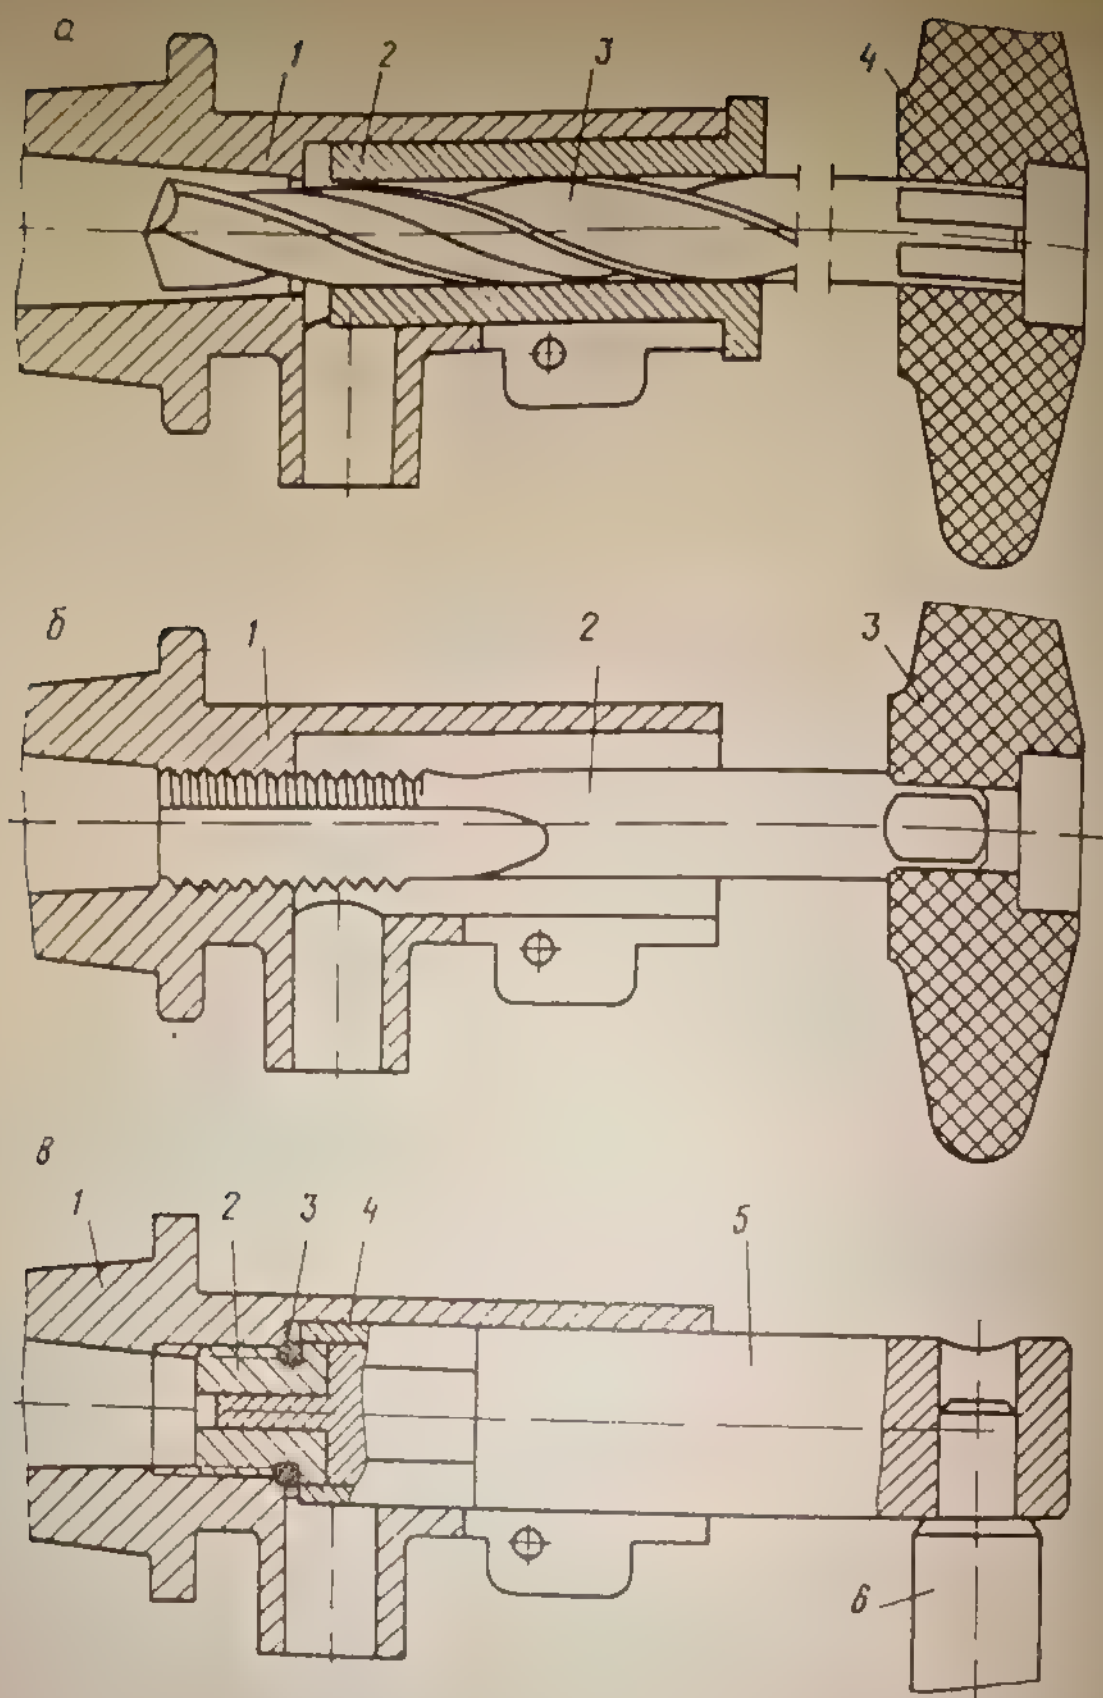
Реставрация разрушенного седла в корпусе поплавкового клапана
